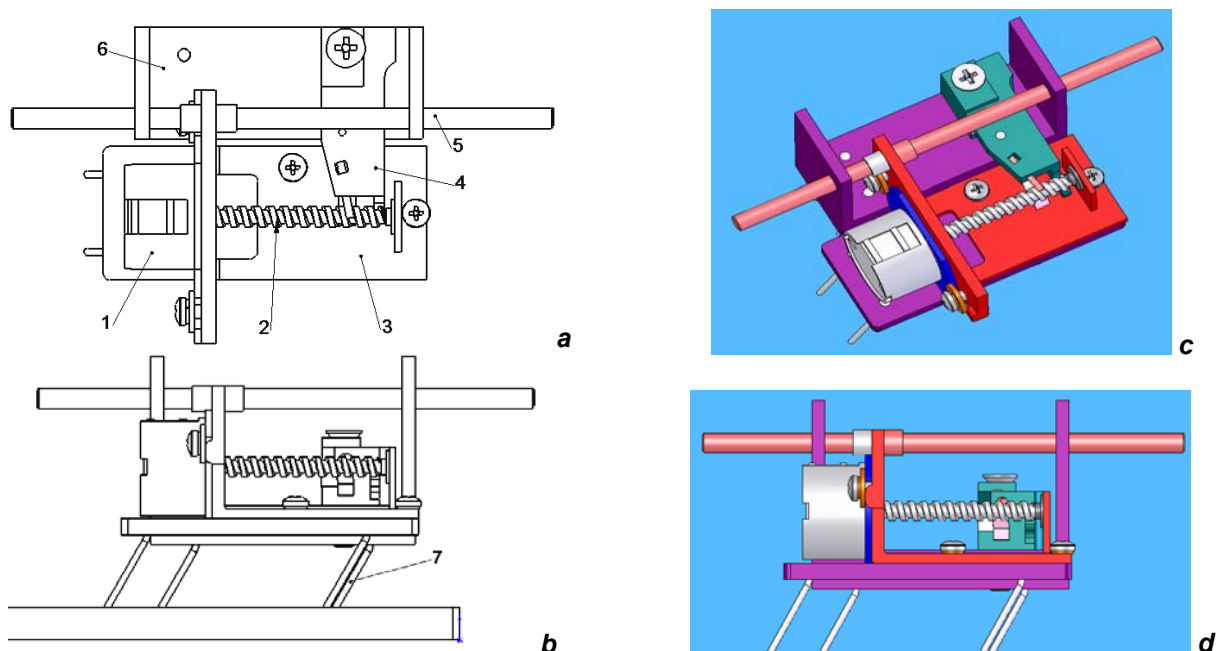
Sistem mobil inchworm cu motor pas cu pas
